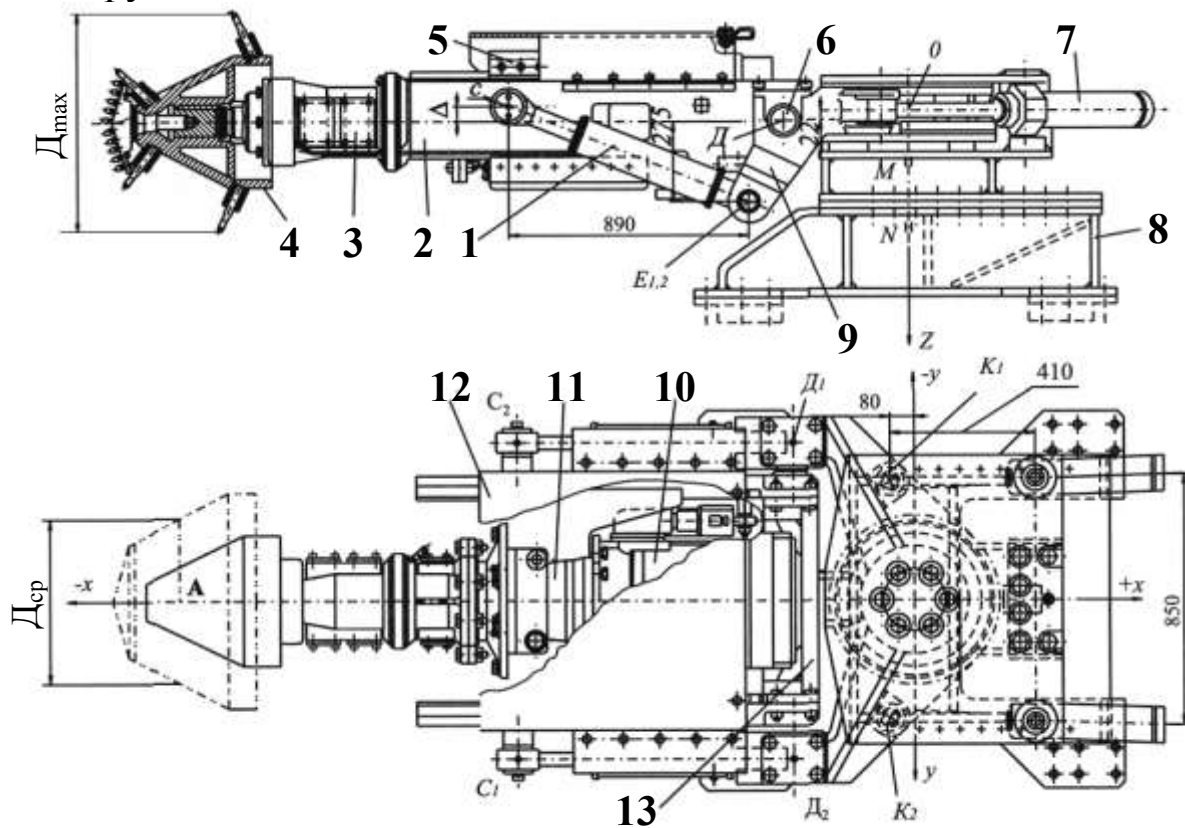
Исполнительный орган механизированного проходческого щита ПЩМ-3,2 комплекса КЩ-3,2Б
